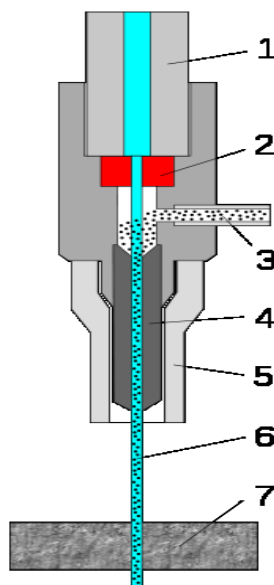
Схема режущей головки для гидроабразивной резки:
